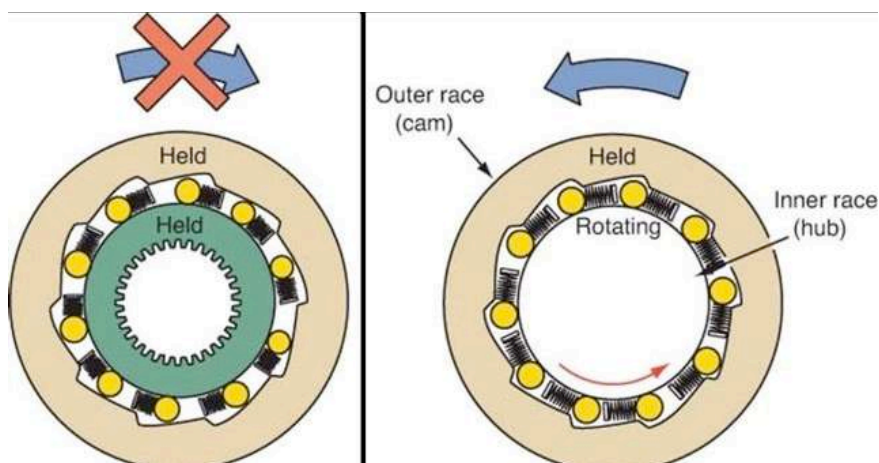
Esquema engranajes de único sentido Fuente [15]
